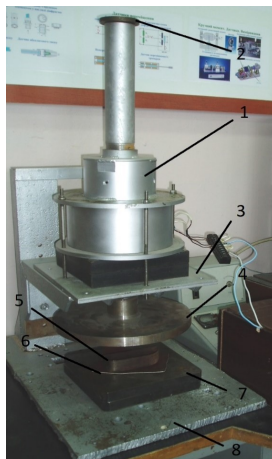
Загальний вигляд пресового обладнання з ЛЕМД з поліпшеними характеристиками: 1 – лінійний електромагнітний двигун; 2 – пристрій утримання якоря; 3 – консоль; 4 – ударник; 5 – різак; 6 – матеріал; 7 – вирубна плита; 8 – станина
